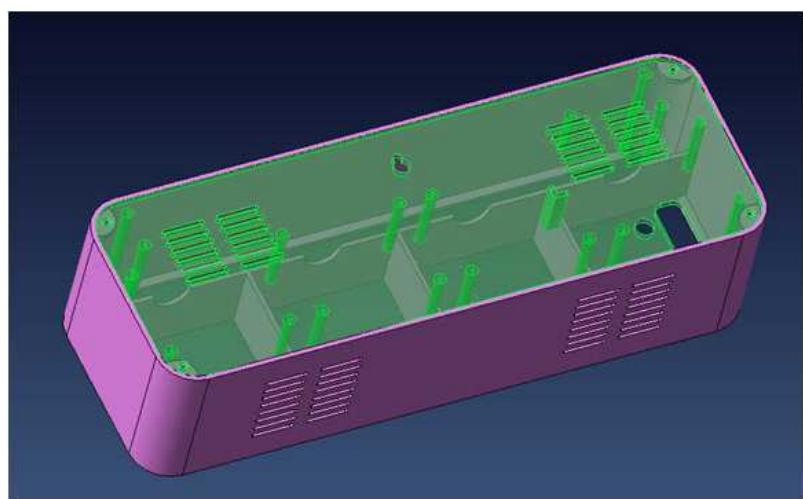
미세먼지신호등 표시부 금형 3D 도면
